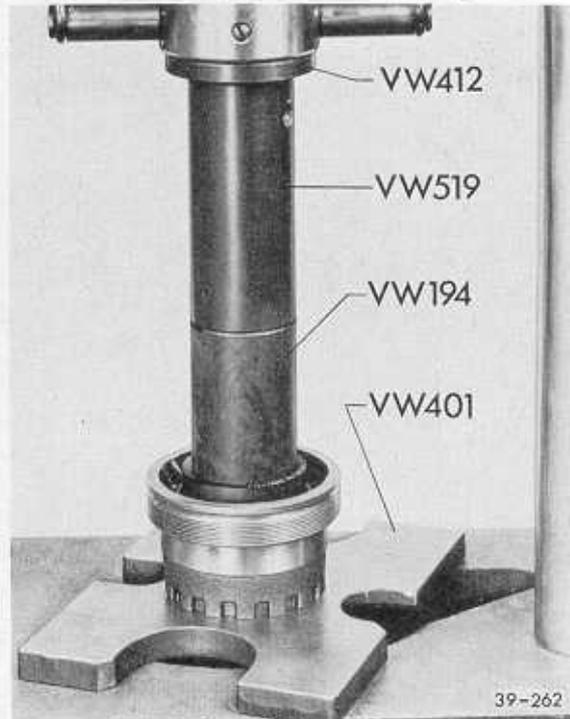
Dichtring für Flanschswelle bündig einpressen.
